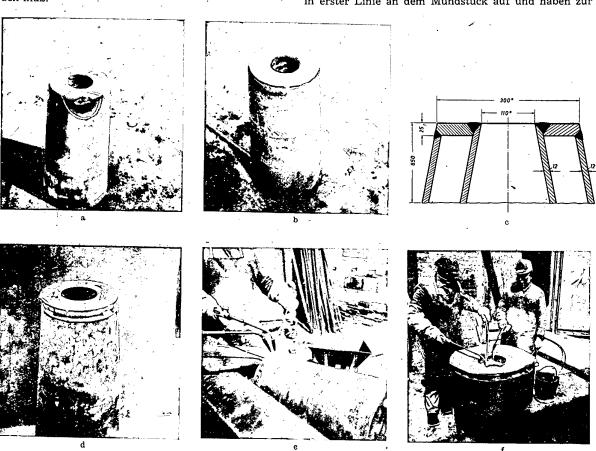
Reparaturschweißung von Hochofenblasformen aus Kupfer (Gewicht etwa 150 kg) a Beschädigte Blasform, b instandgesetzte Blasform, c Schweißnahtanordnung, d Schweißnahtvorbereitung, e Schweißung der Rundnaht, f Schweißung des Mundstückes
